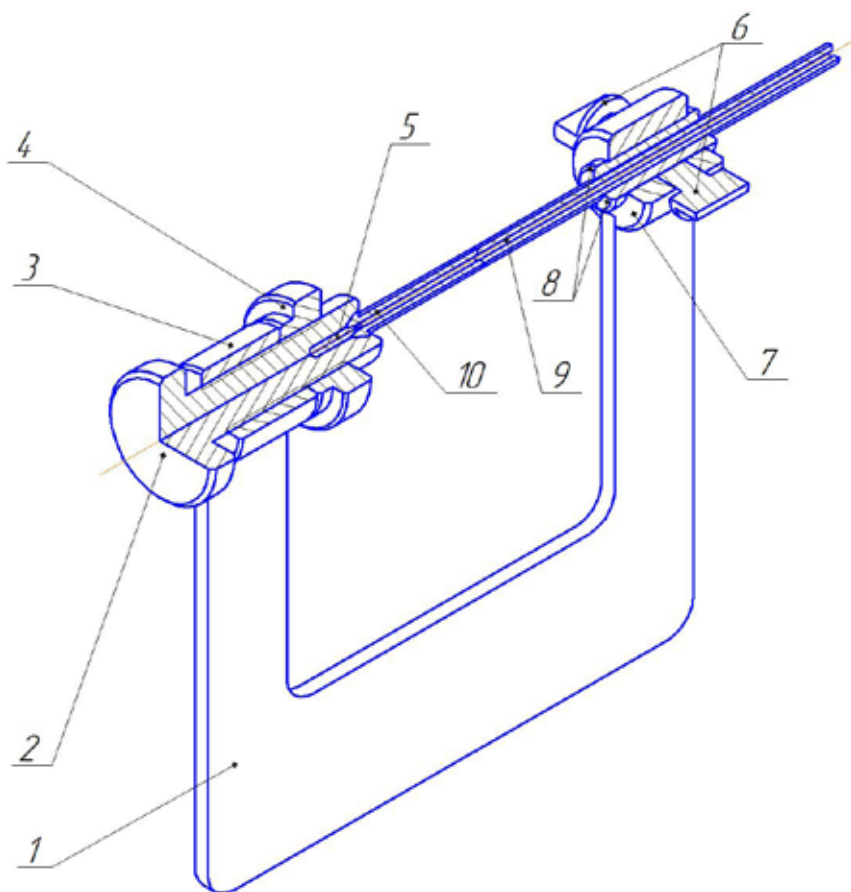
Приспособление для приварки наконечника топливопровода высокого давления
